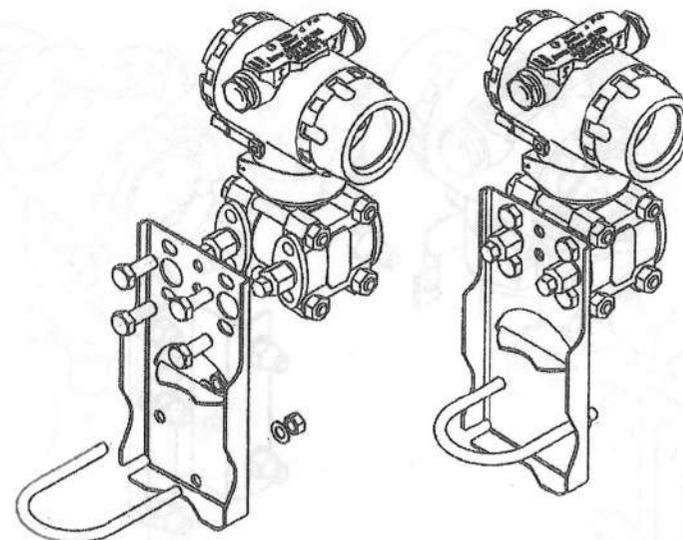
Монтаж датчика на плоский кронштейн, для крепления на трубе (B06)
